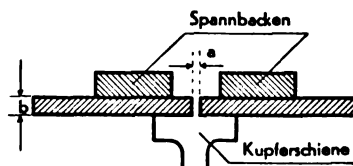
Vorrichtung für das Schweißen von Dünnblechen.
